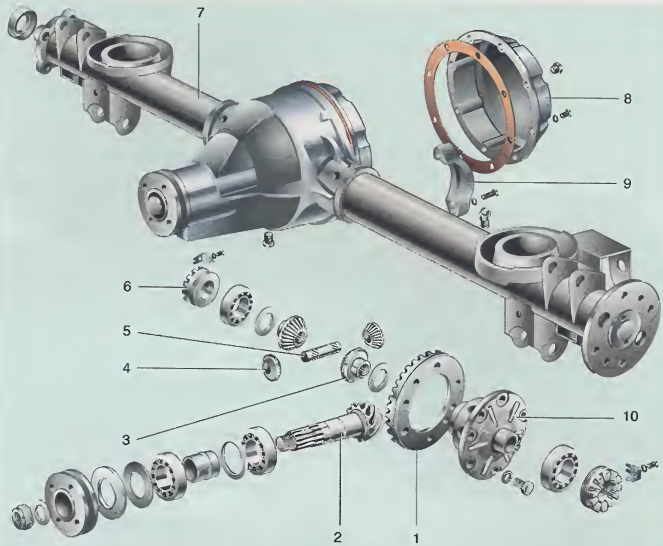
Конструкция заднего моста: 1 – ведомая шестерня главной передачи; 2 – ведущая шестерня главной передачи; 3 – шестерня полуоси; 4 – сателлиты; 5 – ось сателлитов; 6 – регулировочные гайки; 7 – балка заднего моста; 8 – крышка картера; 9 – крышка подшипника; 10 – коробка дифференциала.
